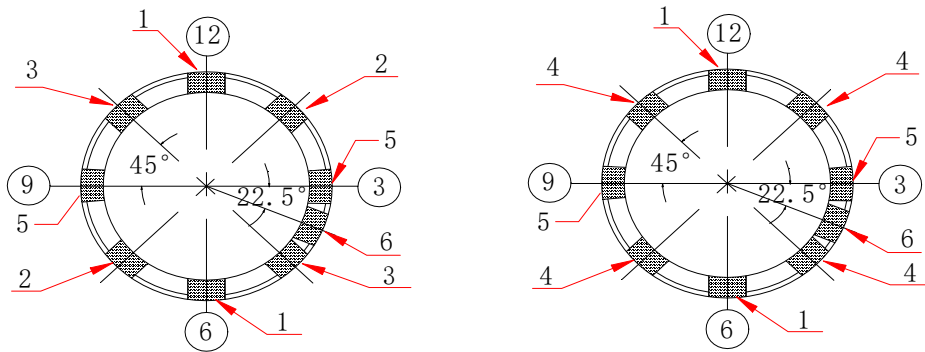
圆管对接接头焊接工艺评定试件及试样取样位置
